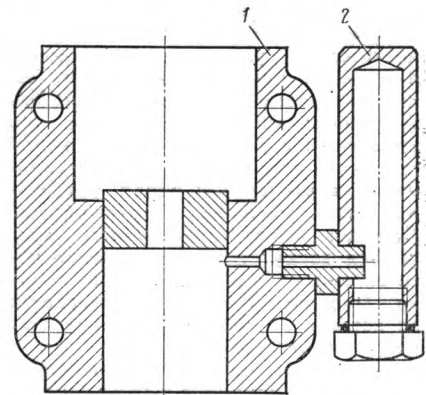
Компенсатор, установленный на корпусе сервомотора регулятора: 1 — корпус сервомотора; 2 — компенсатор
